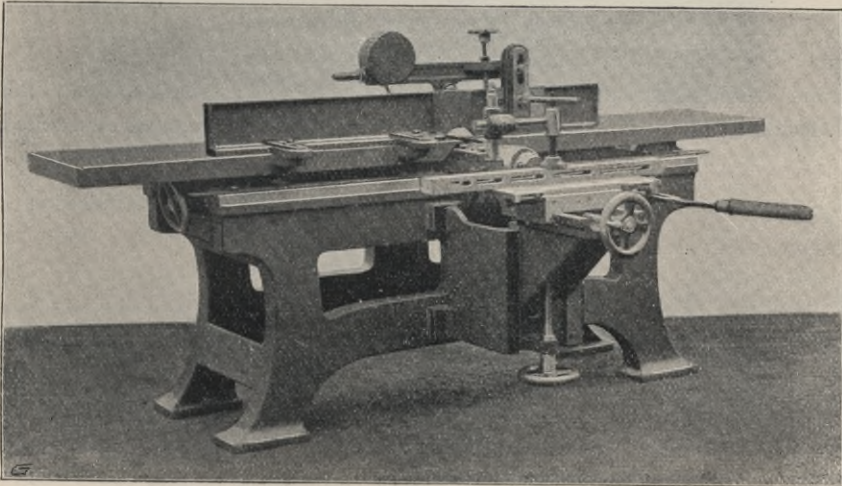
Universal-Abriechthobelmaschine mit Langlochbohrapparat.
